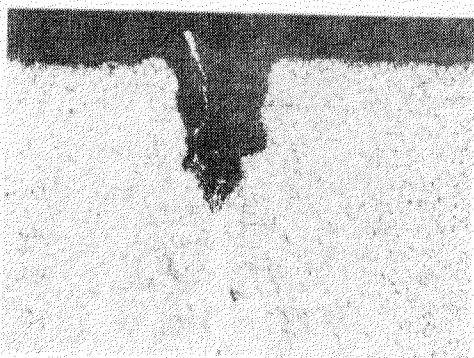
耐薄状腐食性電縫鋼管溶接部の断面 (40℃)
